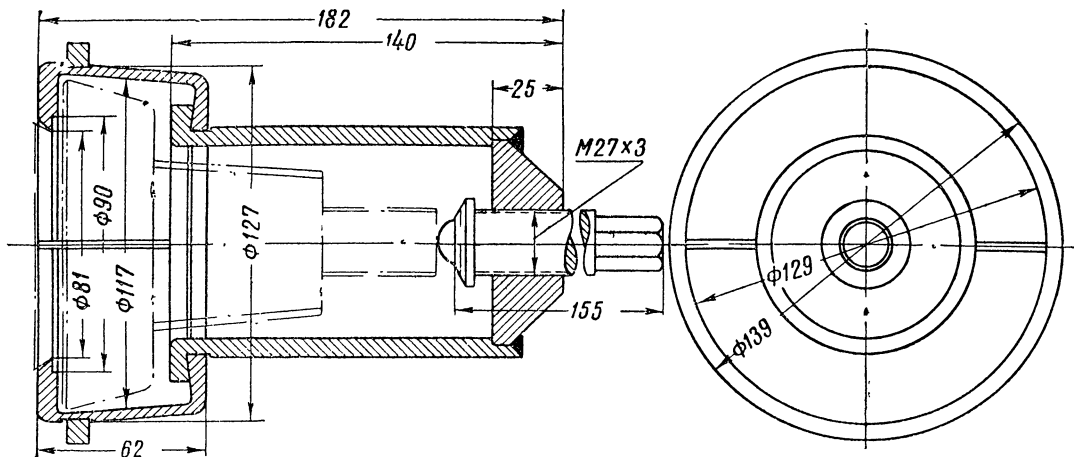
Приспособление для спрессовки конических роликоподшипников с вала большой конической шестерни.
